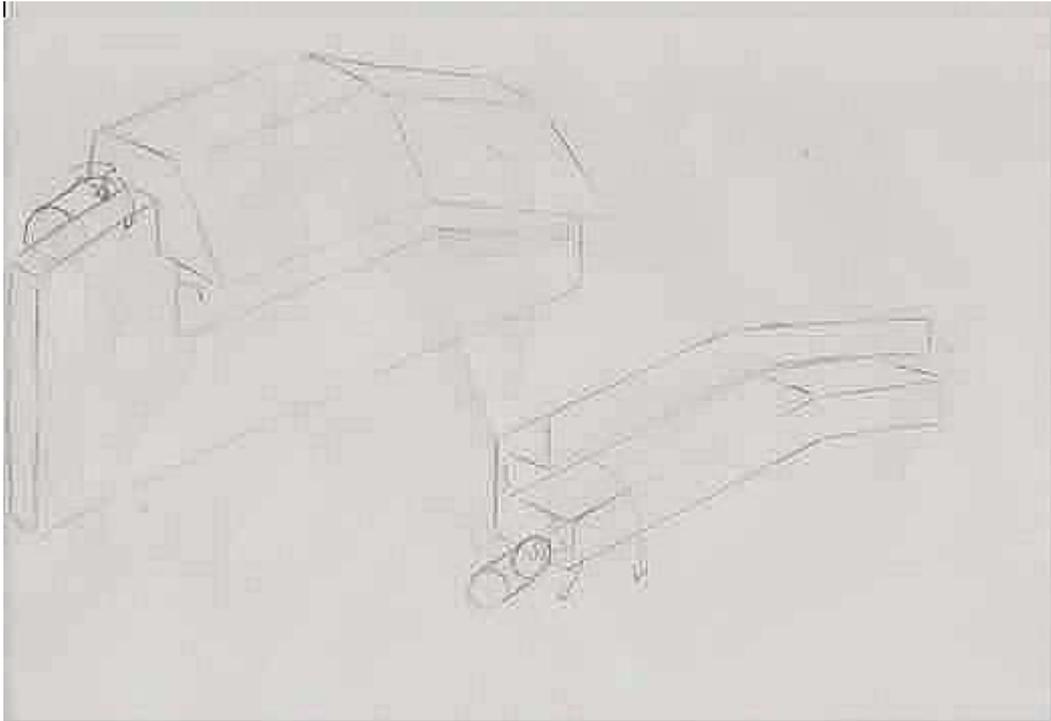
Figura demonstrando a movimentação da calha. Fonte: Autores do projeto.
